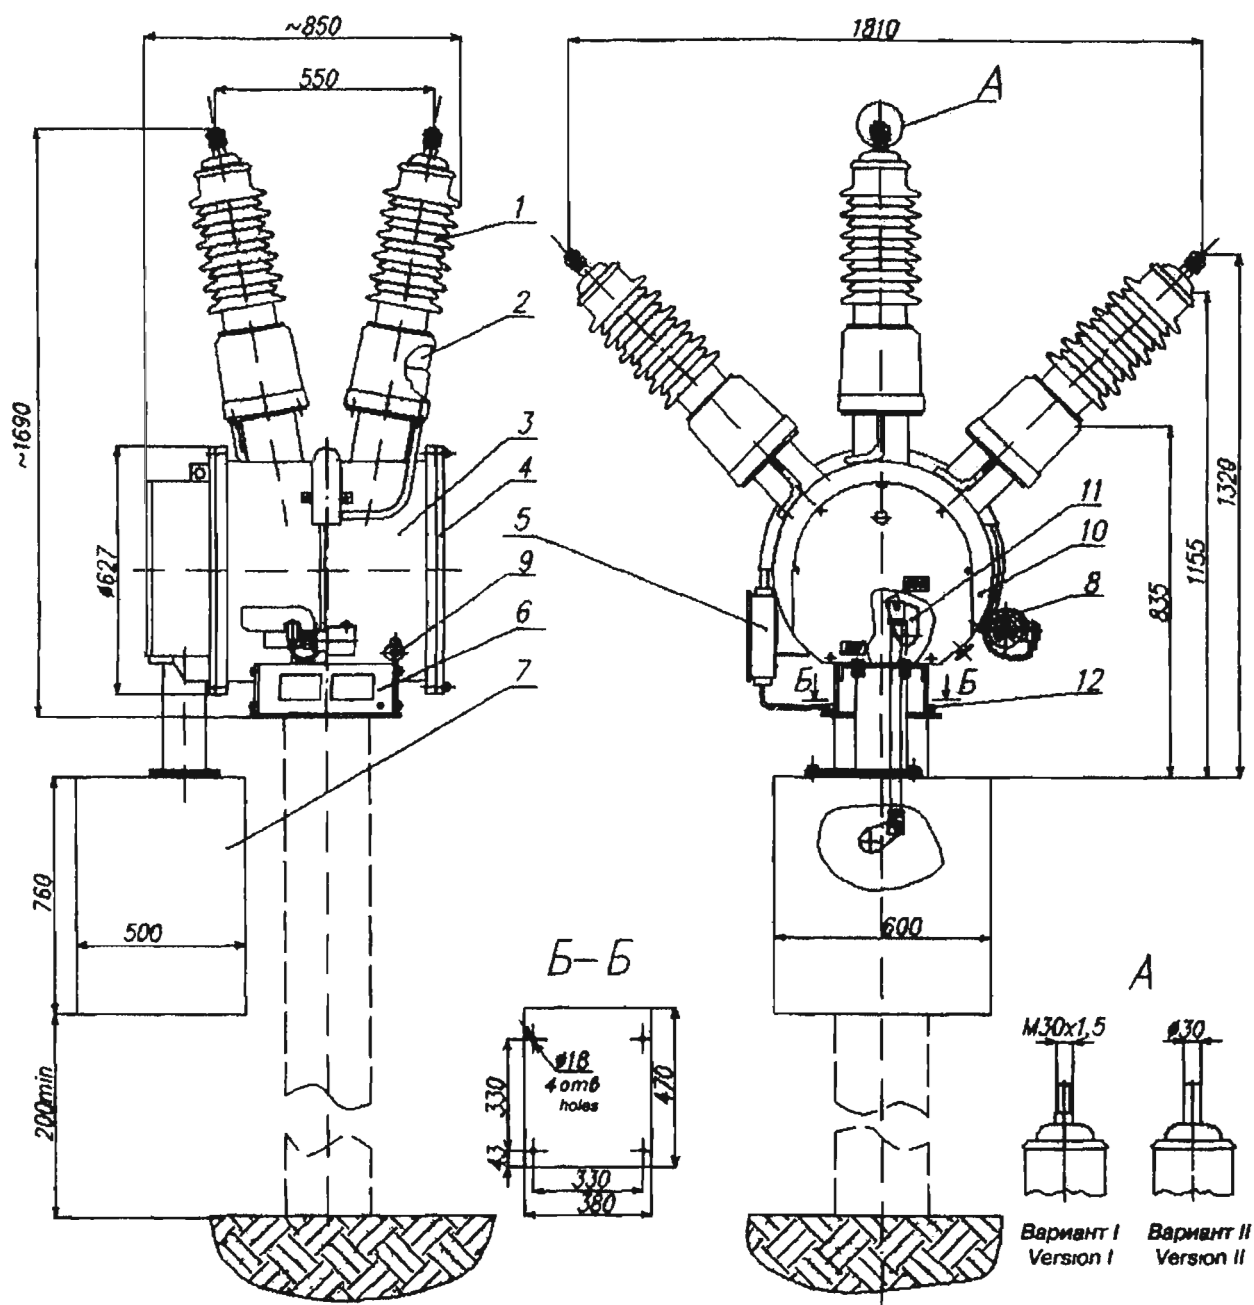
Общий вид и габаритно-установочные размеры выключателя ВГБ-35
